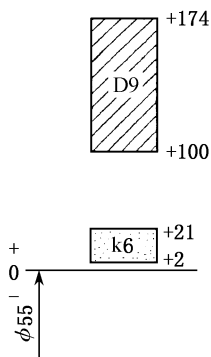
轴套孔与轴颈的公差带示意图
